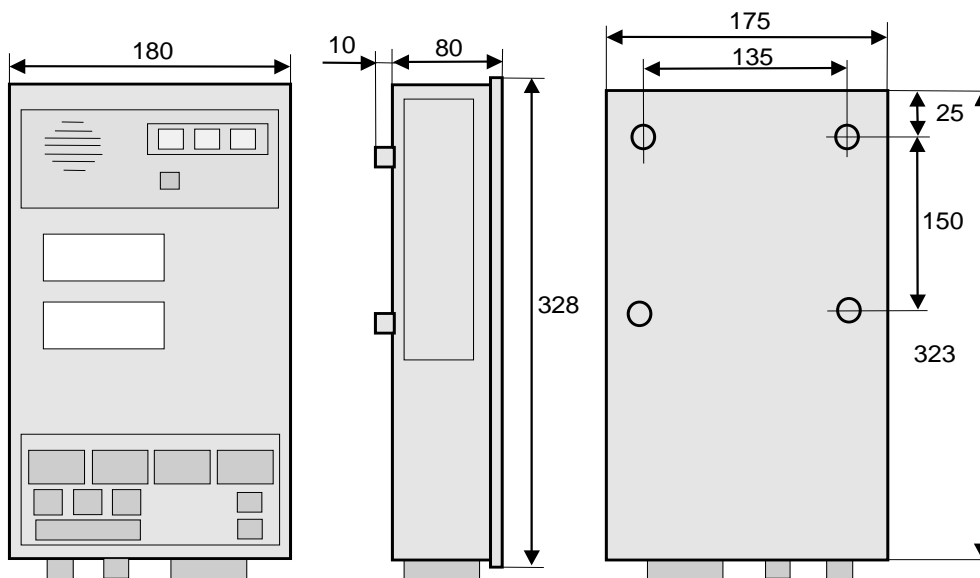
Габаритные и присоединительные размеры БОДа
